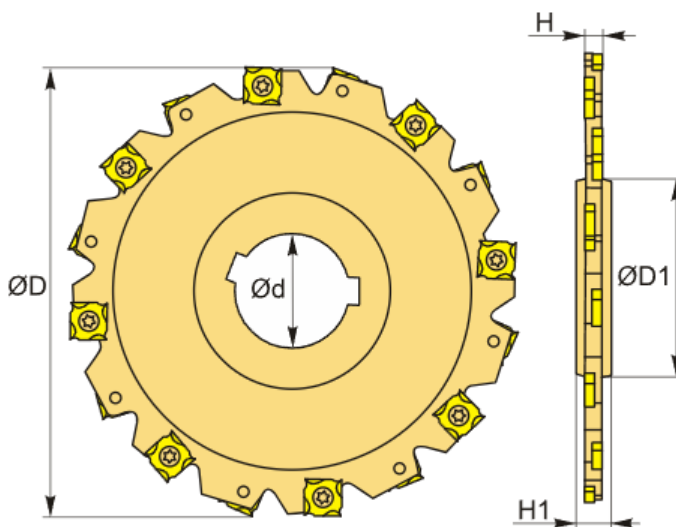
Фреза со сменными твердосплавными пластинами
